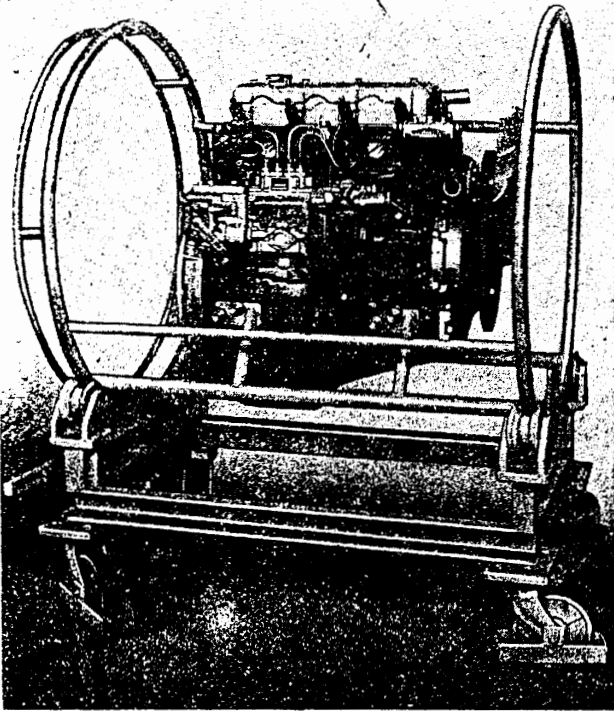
Motor im Montagewagen (Werkzeug Nr. 324.020-M 110)
